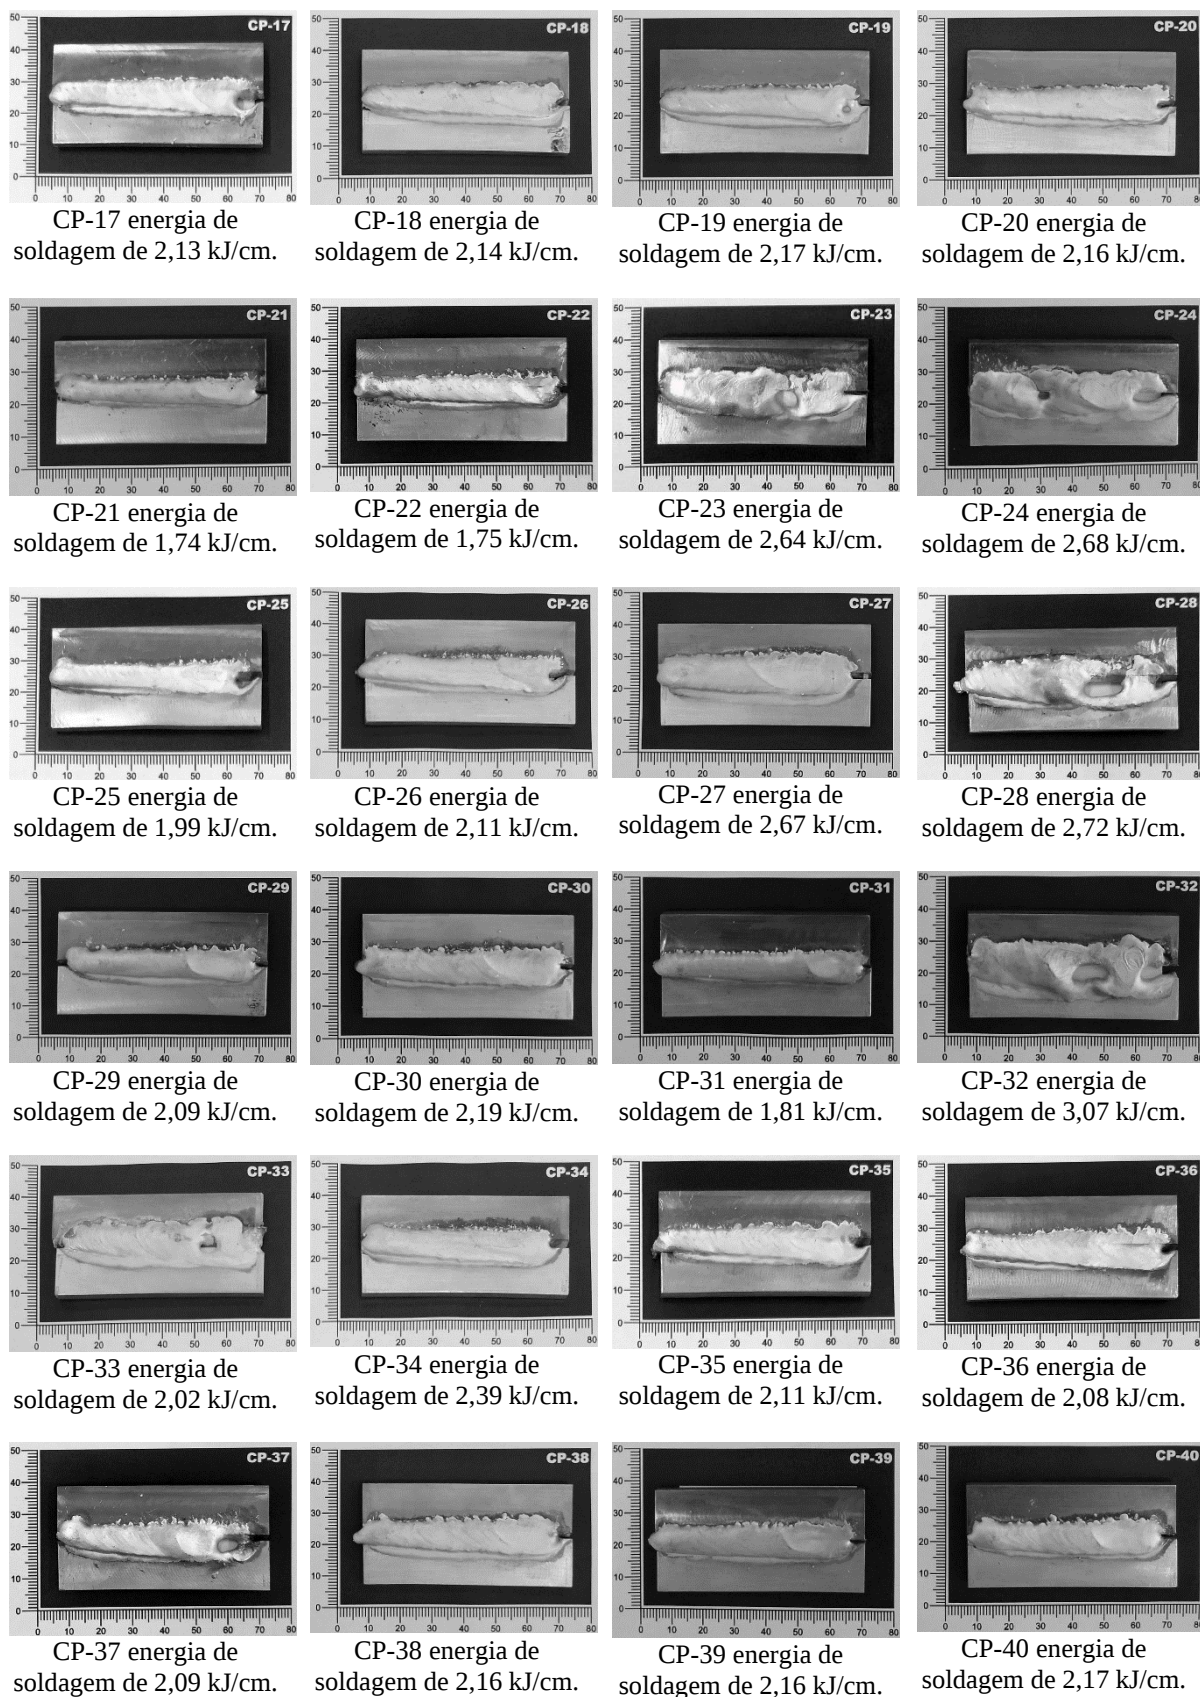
Corpos de prova soldados e suas respectivas energias de soldagem.
